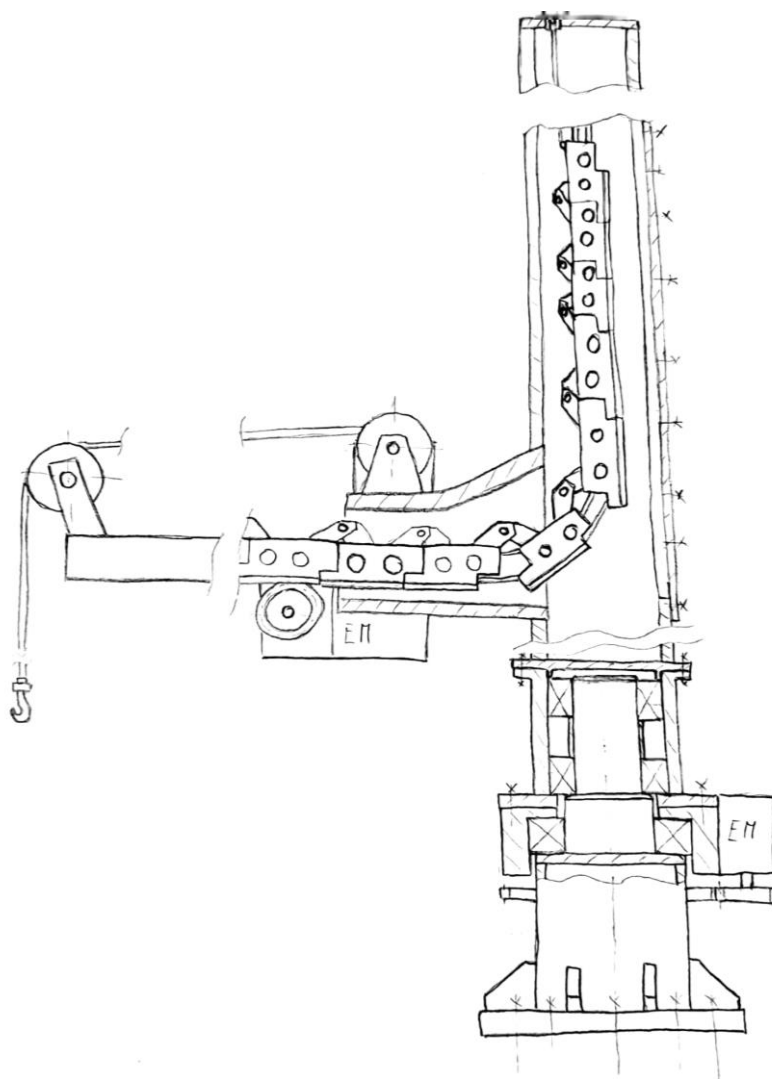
COLUMN FOR LIFTING LOADS- prikaz spajanja članaka [14]
